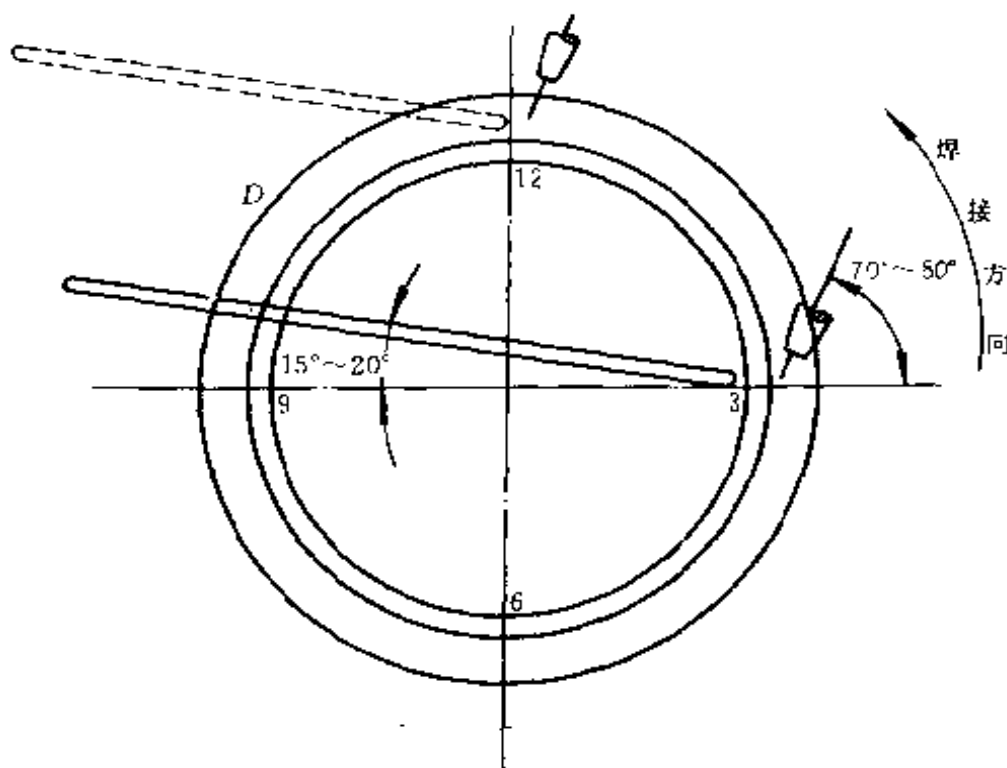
小管水平固定对接时钟 3 点位置逆时针至 12 点位置焊缝的 TIG 焊
